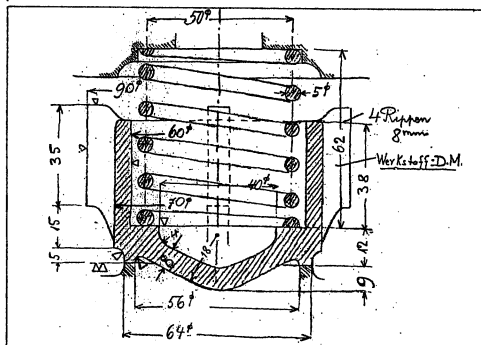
/8: Detaillierte Skizze (Schnittdarstellung) mit Hauptmaßen eines Ventiltellers (um 1930)
